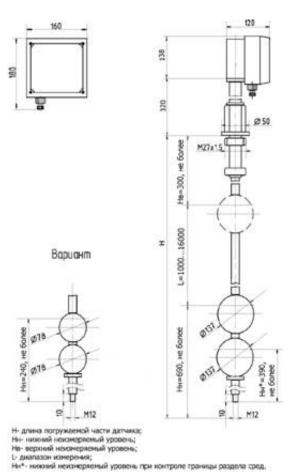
Габаритные и присоединительные размеры преобразователя передающего (ППР)
